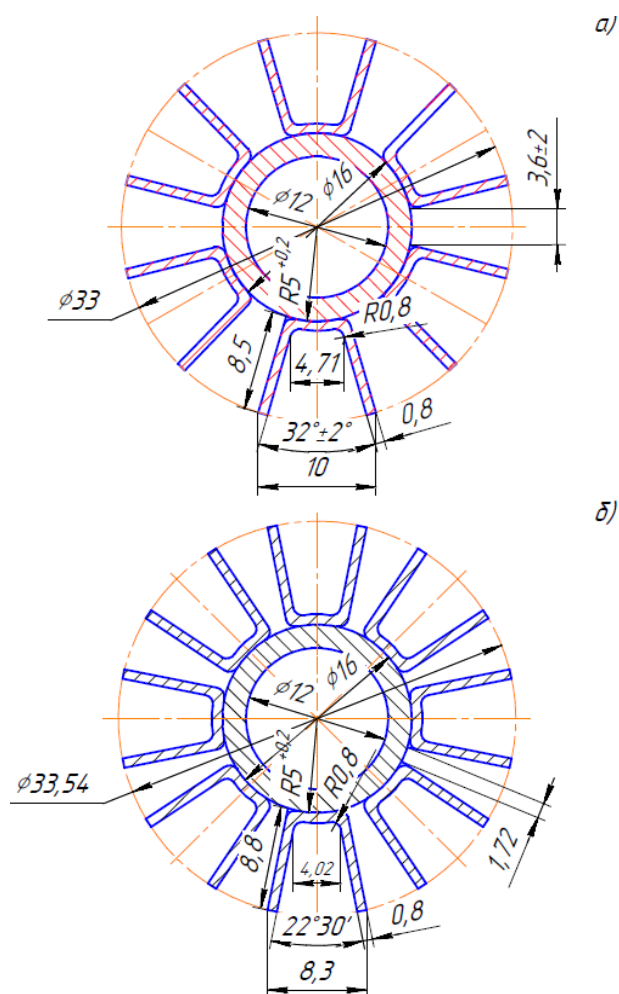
Поперечное сечение теплообменных труб: а) с шестью двойными П-образными ребрами; б) с восьмью двойными П-образными ребрами [Cross section of heat exchange tubes: a) with six double U-shaped ribs; b) with eight double U-shaped ribs]
